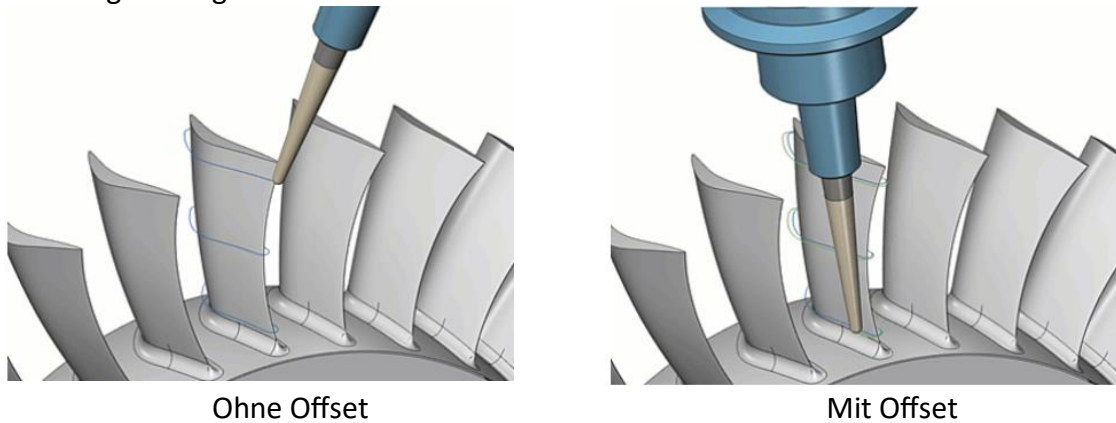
Turbinenschaufel Werkzeugbahnen
